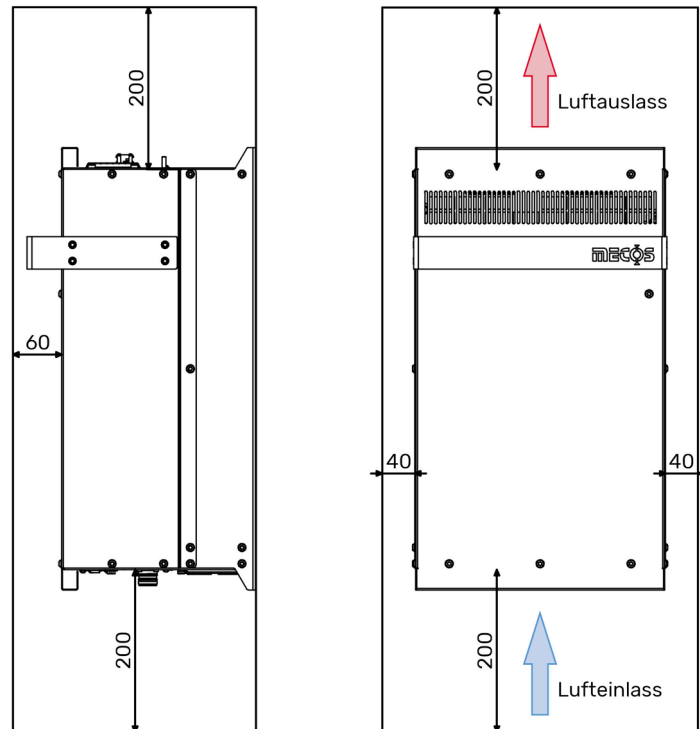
Mindestabstände im Schaltschrank und Luftstromrichtung (Masse in Millimeter)
